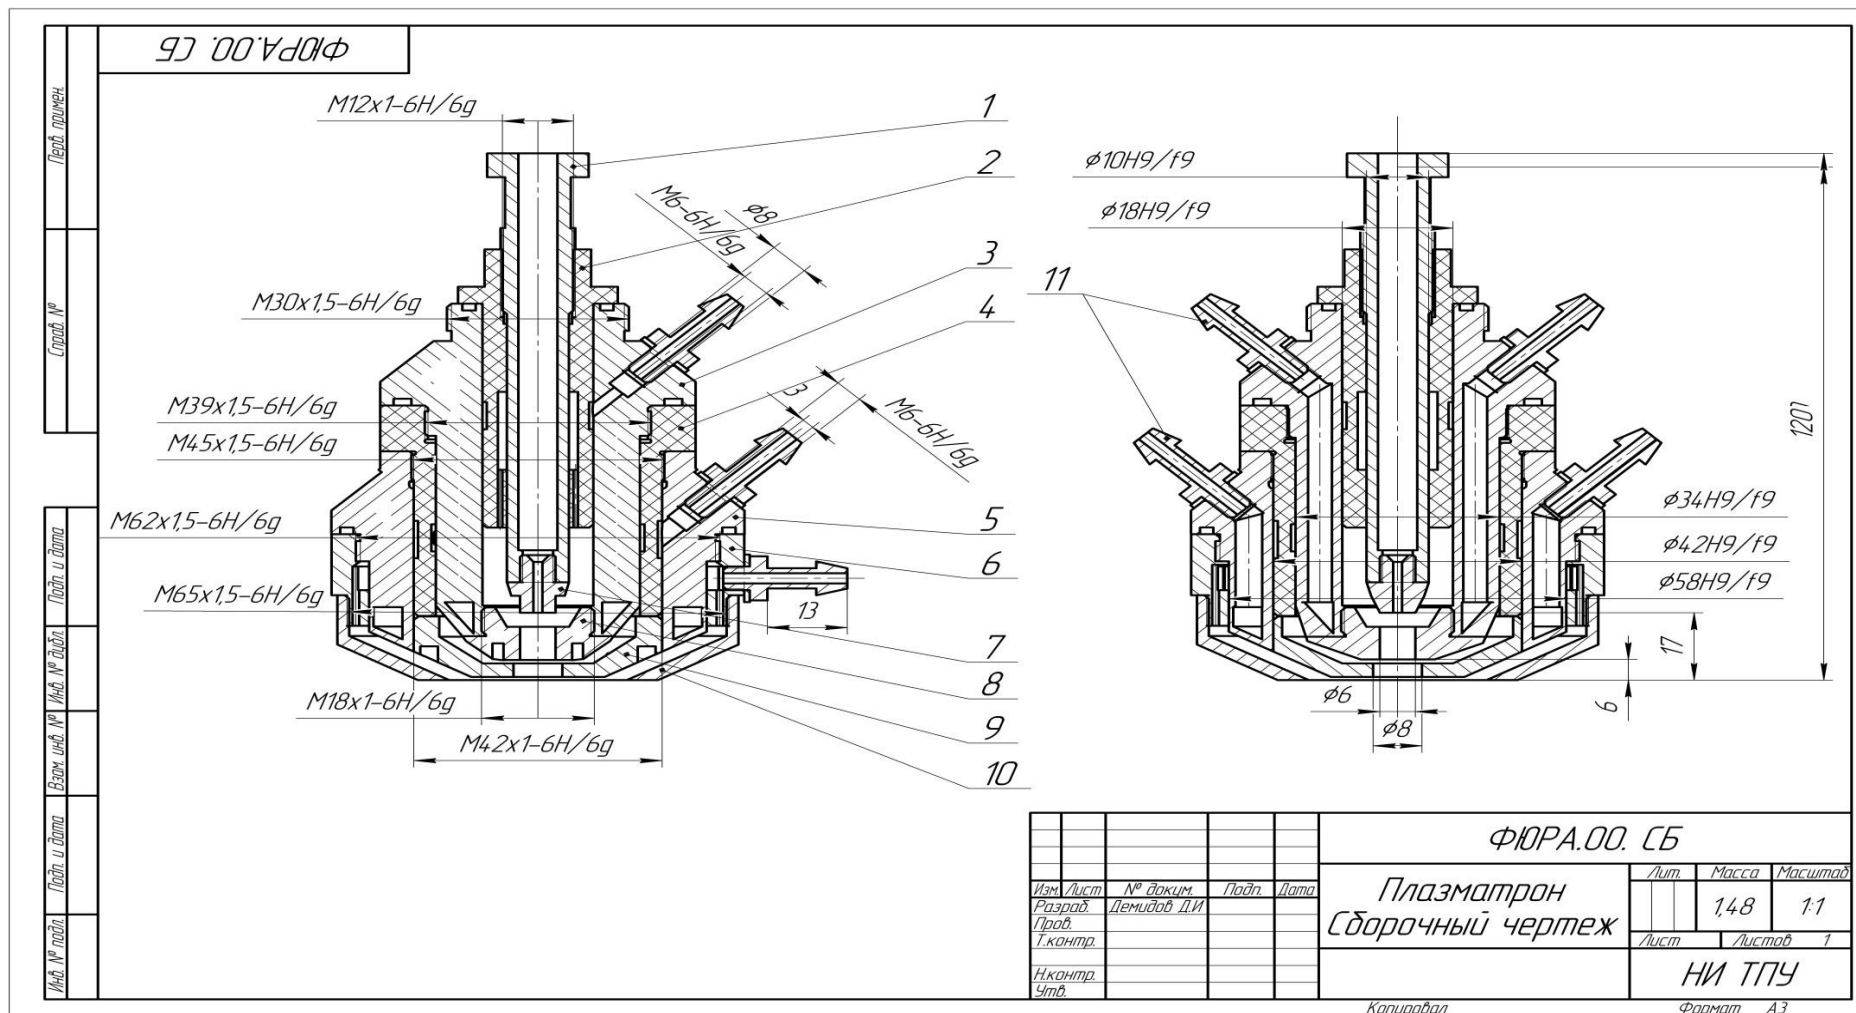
плазматрон для сварки (наплавки) плавящимся электродом (1. Мундштук; 2. Изолирующая втулка; 3. Рубашка охлаждения кольцевого анода; 4. Рассекатель стабилизирующего газа; 5. Рубашка охлаждения стабилизирующего сопла; 6. Рассекатель защитного газа; 7. Токоподводящий наконечник; 8. Кольцевой медный анод; 9. Стабилизирующее сопло. 10. Защитное сопло; 11. Штуц
